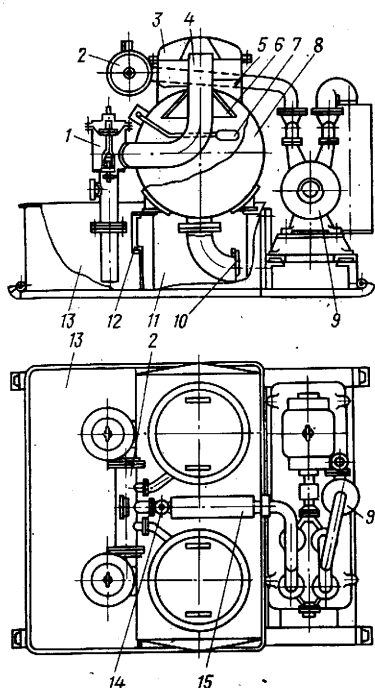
Двухкамерный вакуумный дегазатор типа ДВС-II
